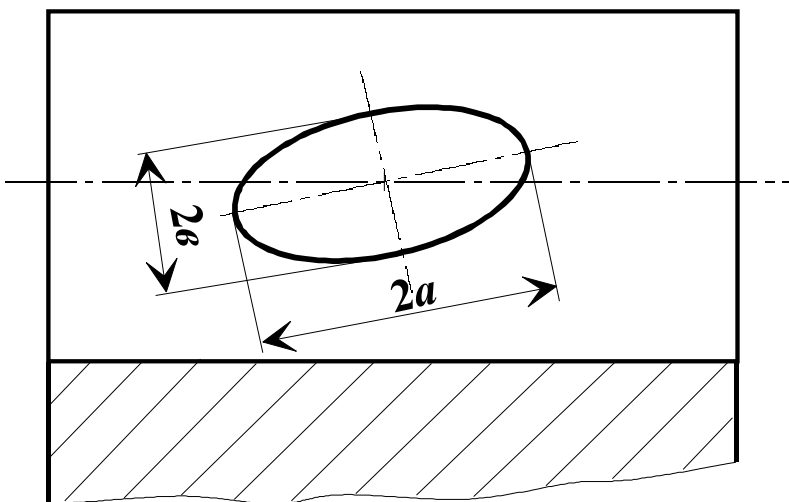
Форма и размеры пятна контакта поверхностей зубьев шевера и колеса
